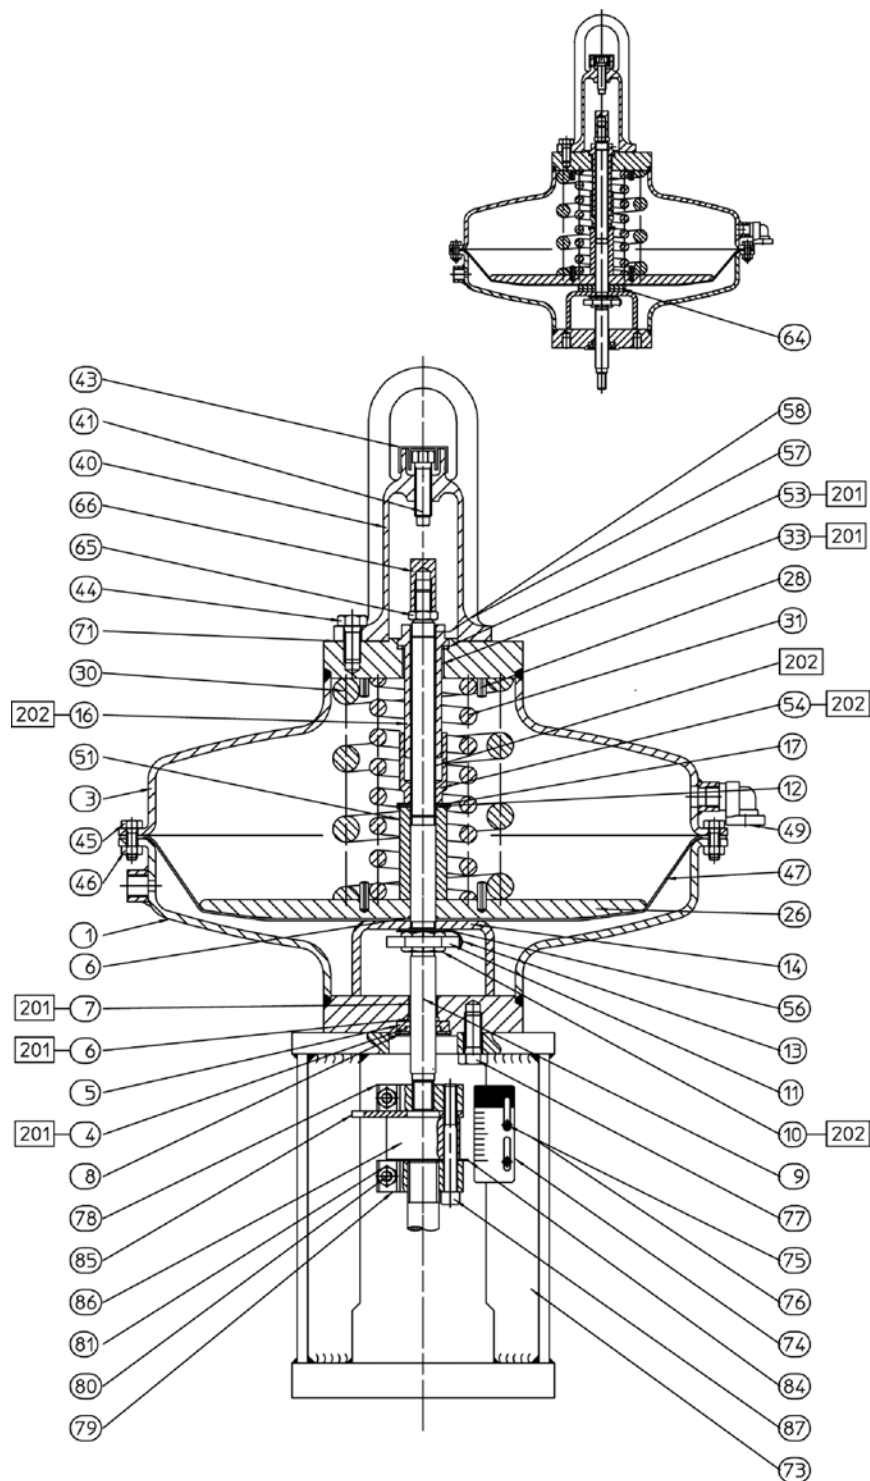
Привод Fisher 3025 размера P462, воздух открывает
